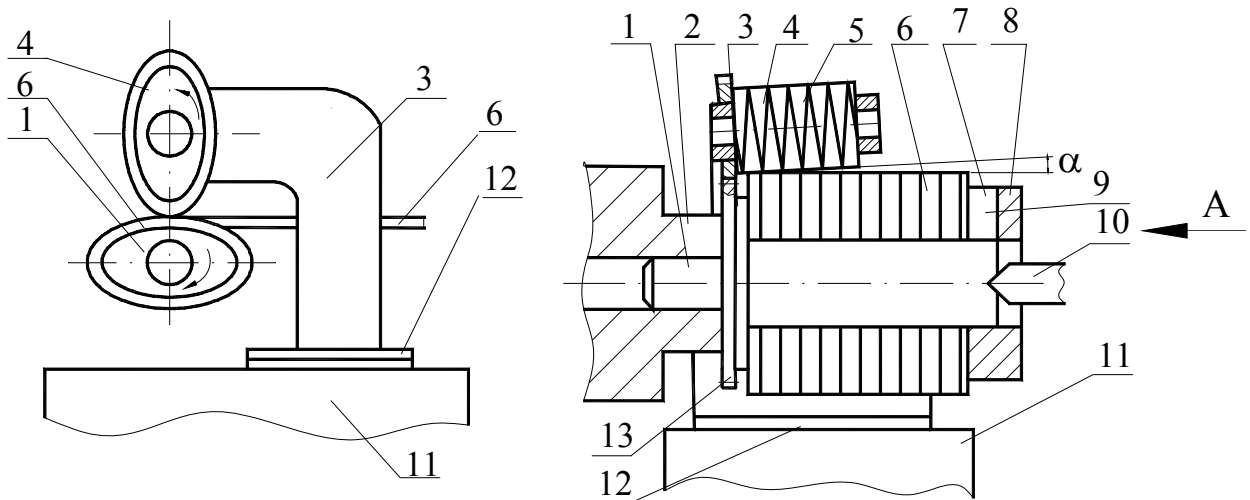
Схема пристрою для виготовлення збірного зубчасте навивне колесо
